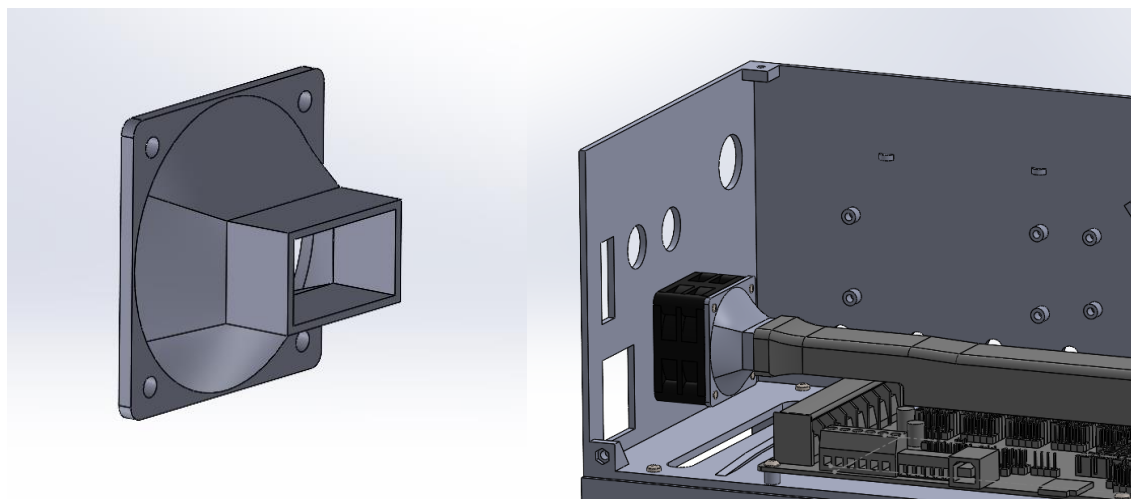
Bocal para ventilador à esquerda; bocal assembledo à direita.
